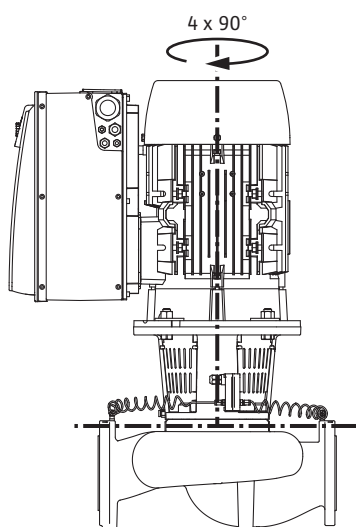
Přípustné polohy instalace se svislým hřídelem motoru
